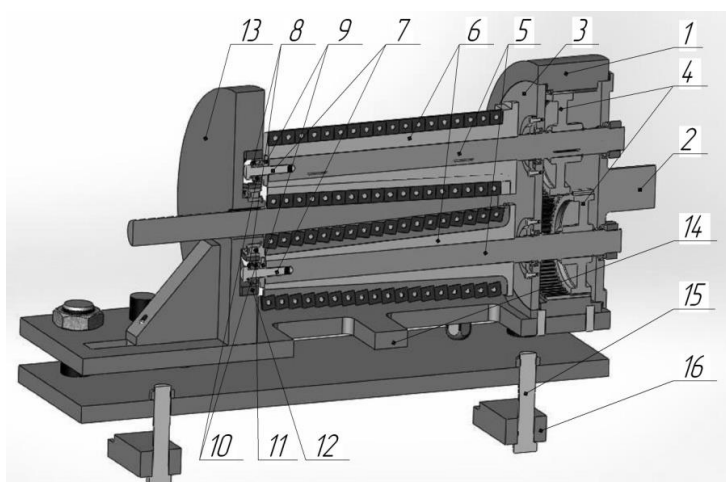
Устройство для формообразования профильной части пружин железнодорожного транспорта: 1 – зубчатое колесо; 2 – планшайба; 3 – крышка; 4 – планетарное зубчатое колесо, 5 – вал; 6 – резцовый блок; 7 – болт крепёжный; 8 – шайба; 9 – шайба; 10 – подшипник; 11 – подшипник; 12 – подшипник; 13 – задняя стенка; 14 – плита; 15 – болт; 16 – планка крепёжная
